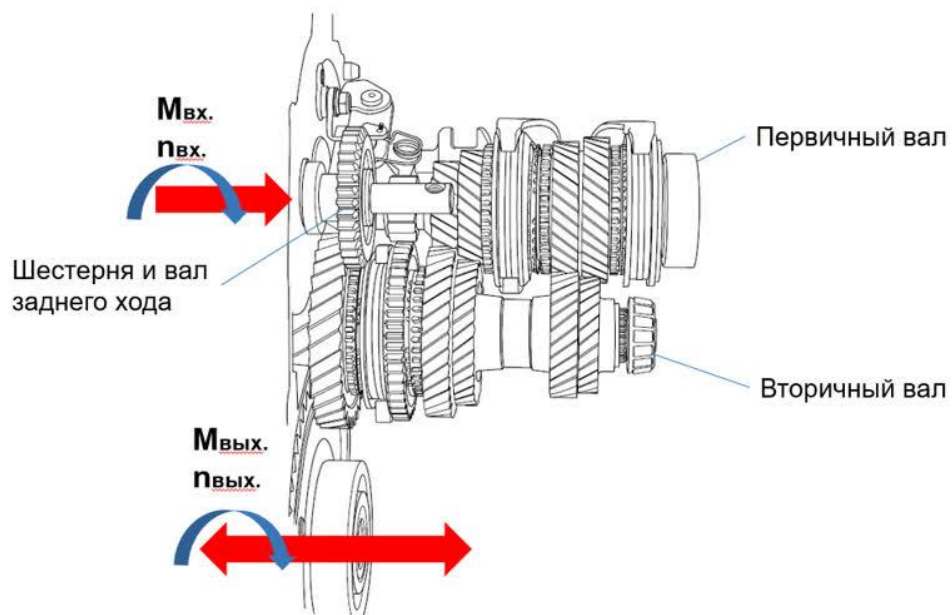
Схема двухвальной коробки передач: устройство и принцип работы
